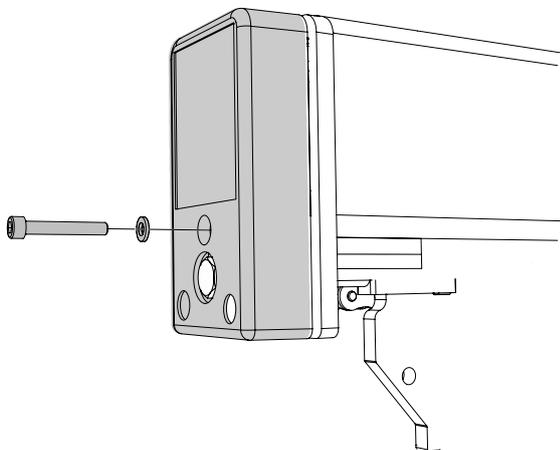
Couvercle d'extrémité du profilé du tube porteur
